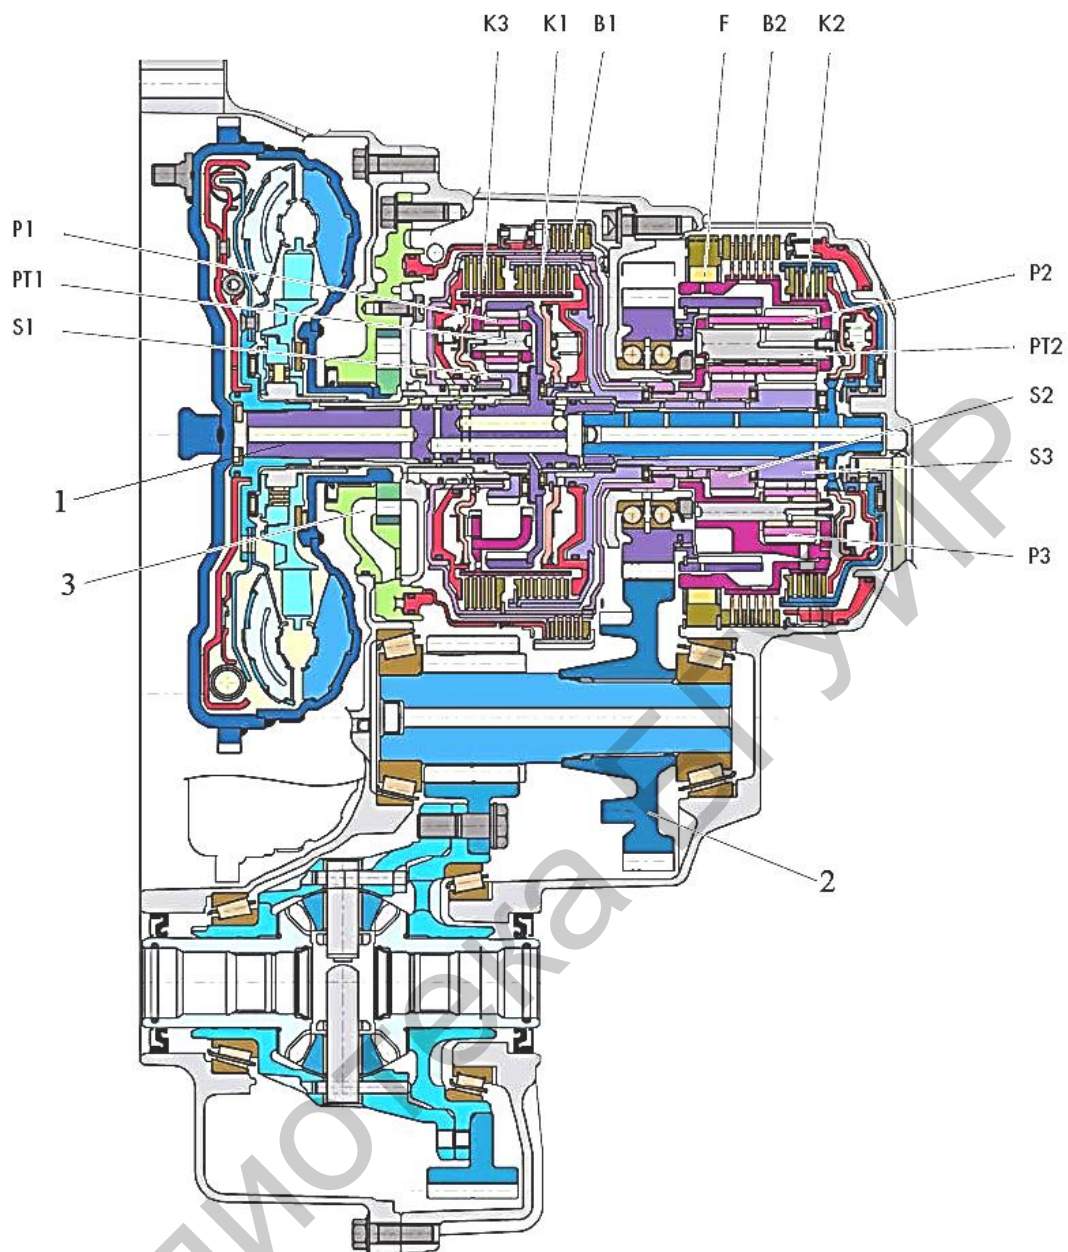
Разрез автоматической шестиступенчатой коробки передач O9G:
